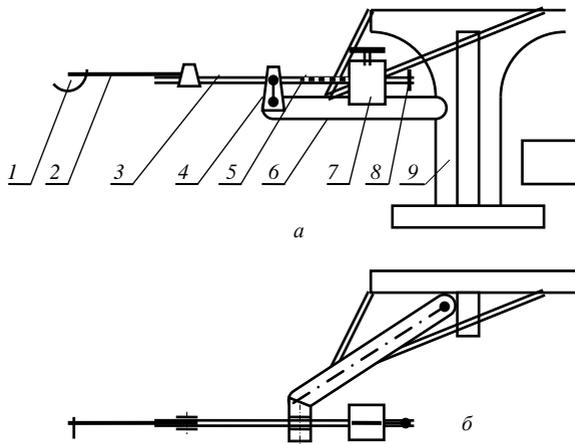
Схема люнета: *а* – вид сбоку и *б* – вид сверху;
